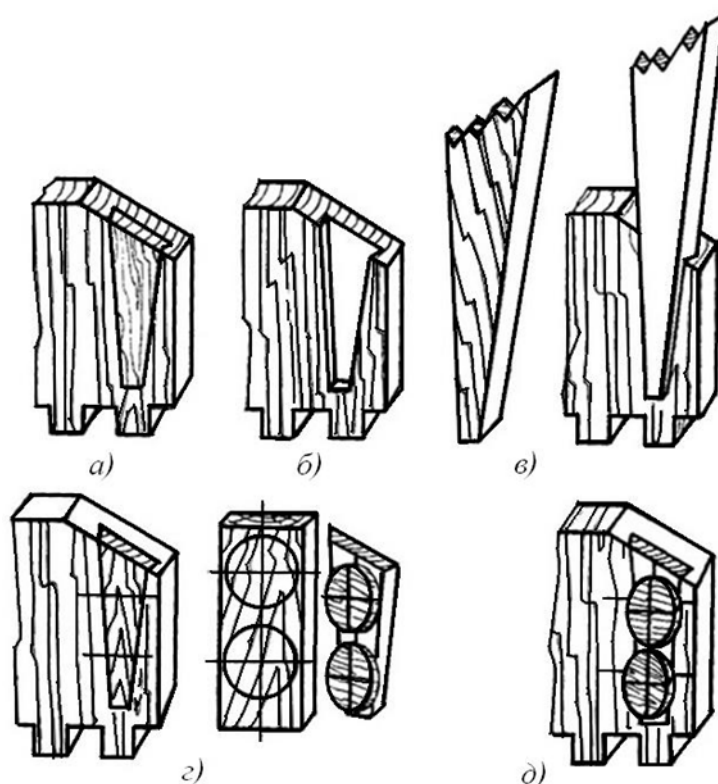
Изготовление (а - д) клинового крепления отъемных частей модели
